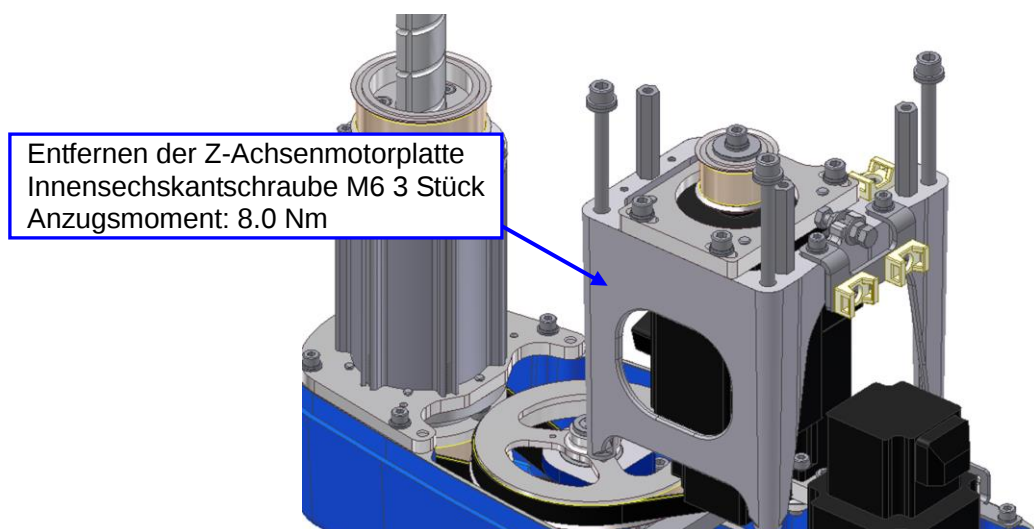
Entfernen der Z-Achsenmotorplatte
